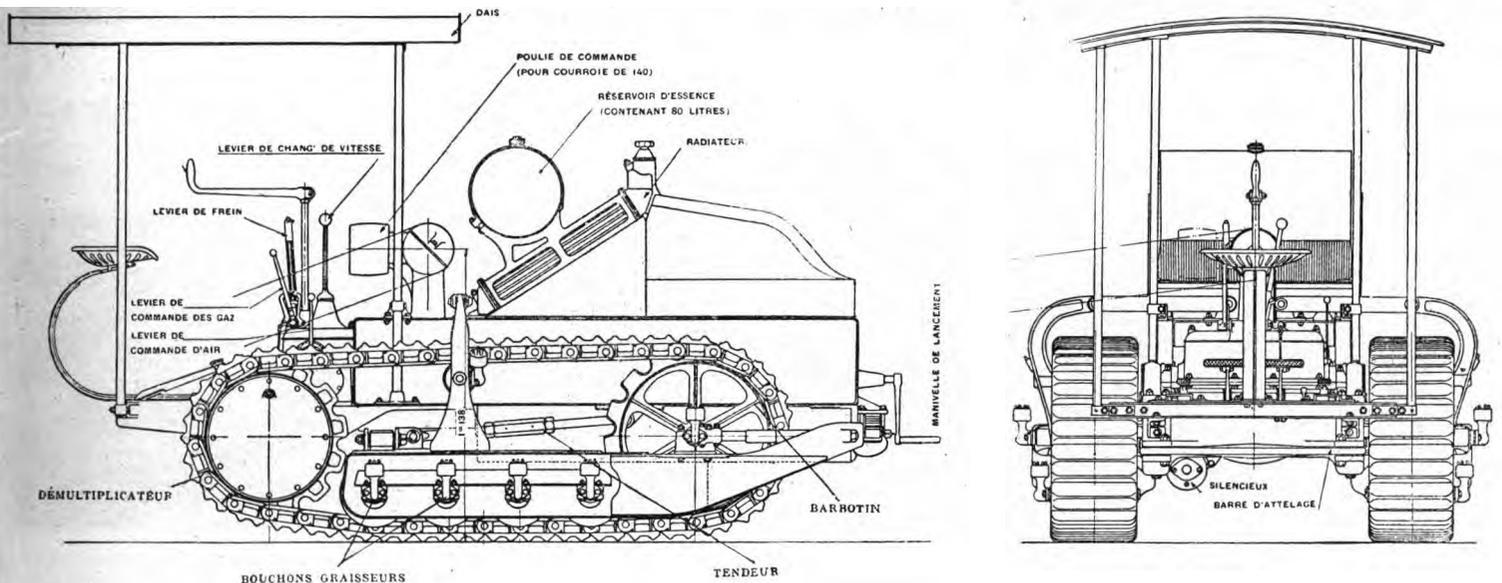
Coupe et élévation d'un tracteur à chenilles (Renault)
